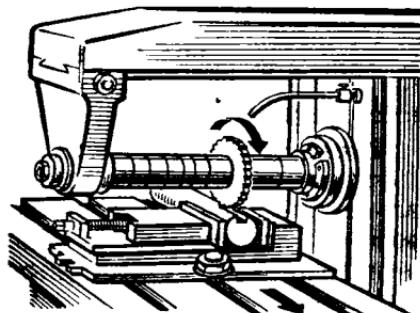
Фрезерование сквозного паза дисковой фрезой.
